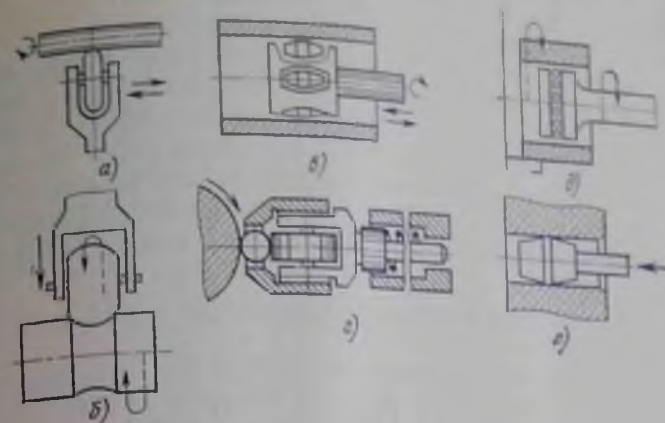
Схемы статического поверхностного пластического деформирования деталей горного оборудования:
